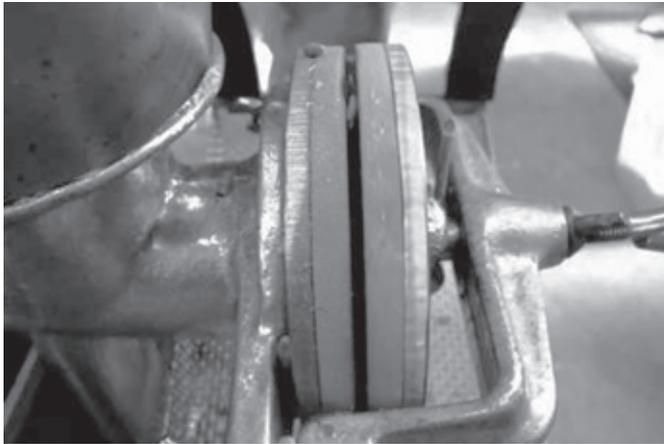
Das Bild zeigt ein Detail. Gut ersichtlich sind die zwei Scheiben aus Gummi. Wichtig ist auch die Spalte dazwischen. Quelle: Jeffrey Funk
